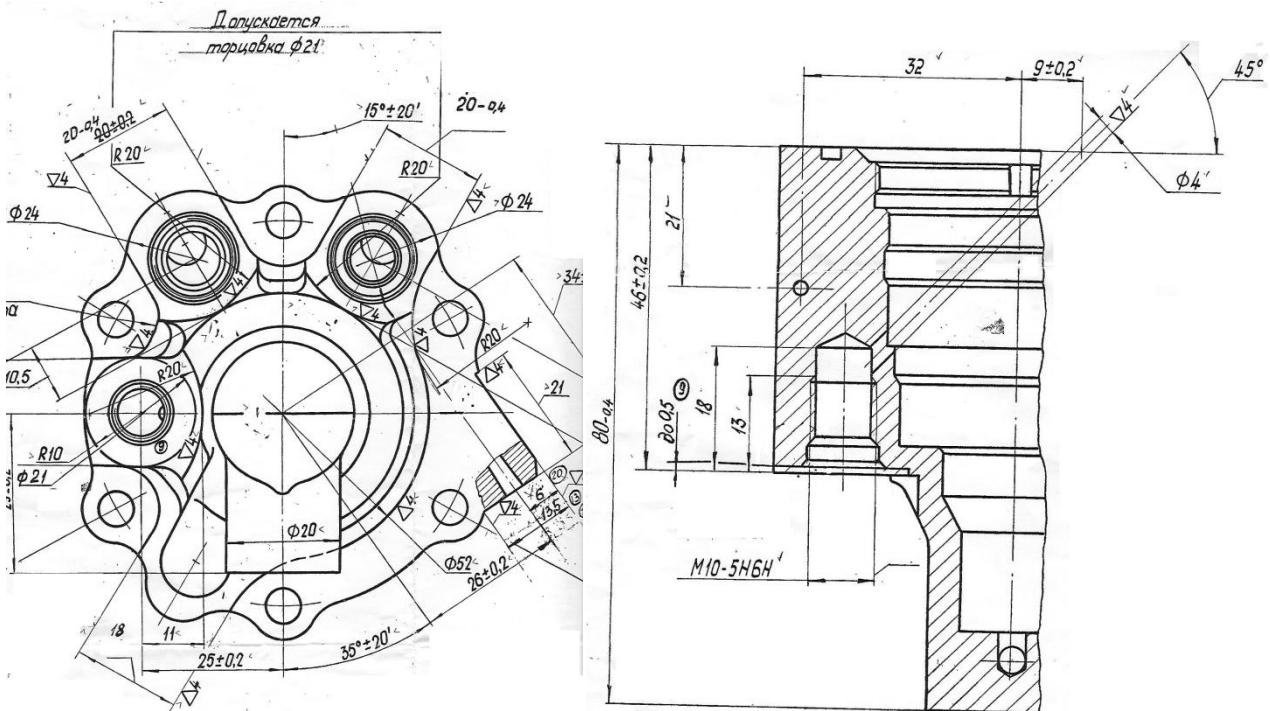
Чертеж детали «Корпус регулятора ТНА»
